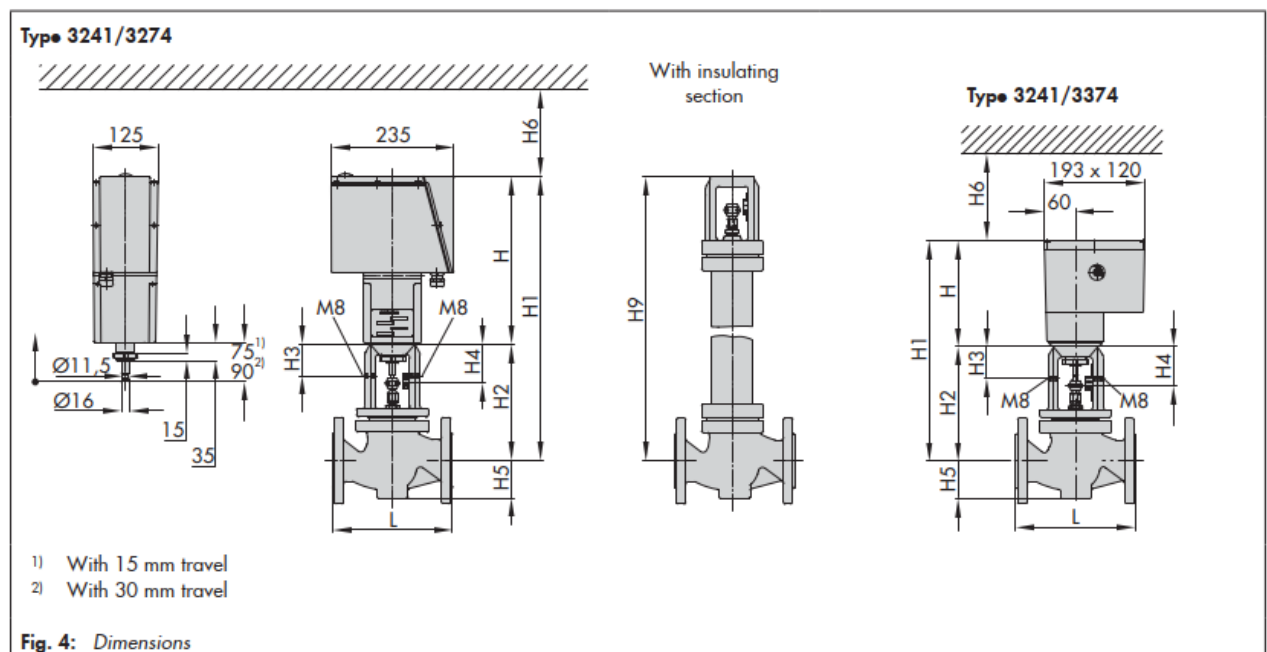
Габаритні розміри клапанів Тип 3241/3374
